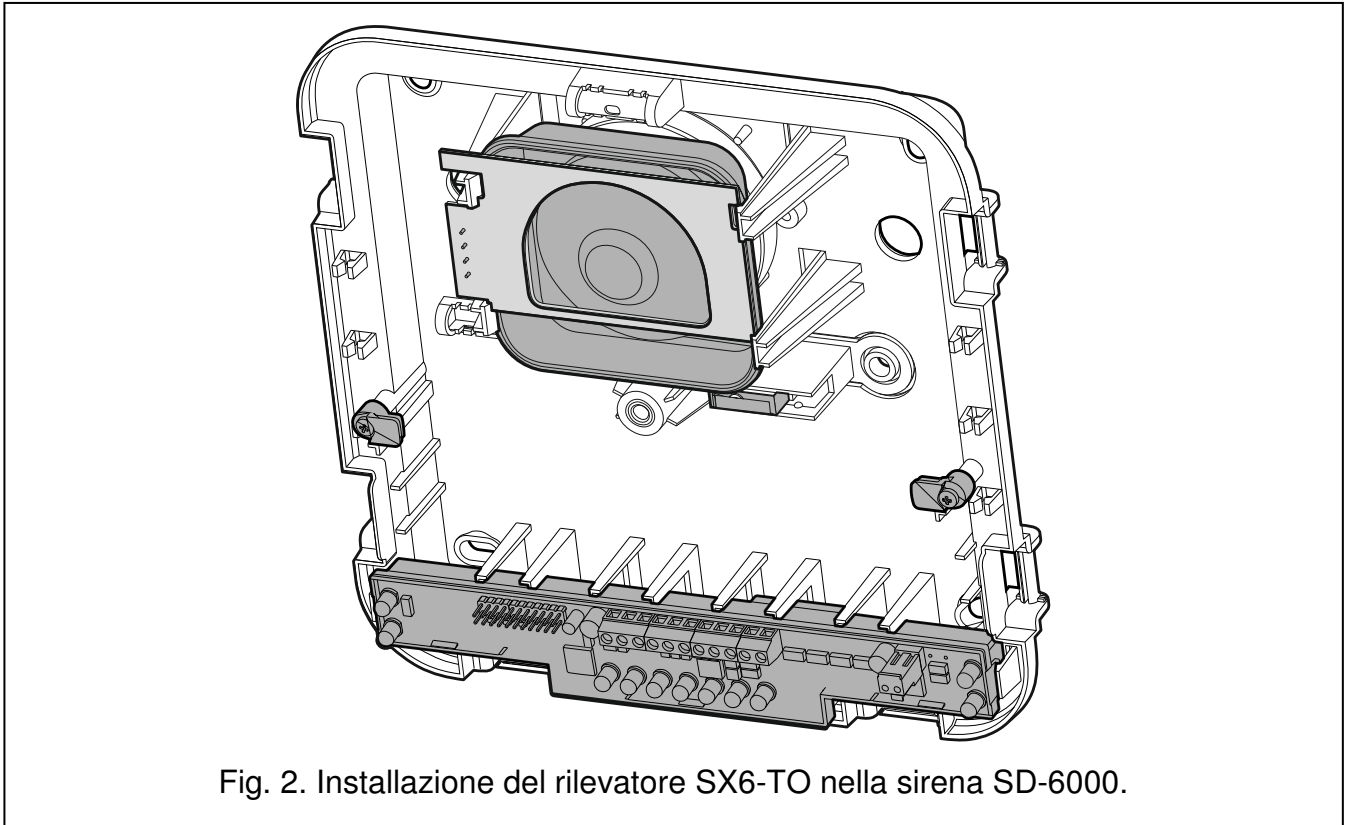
Installazione del rilevatore SX6-TO nella sirena SD-6000.
